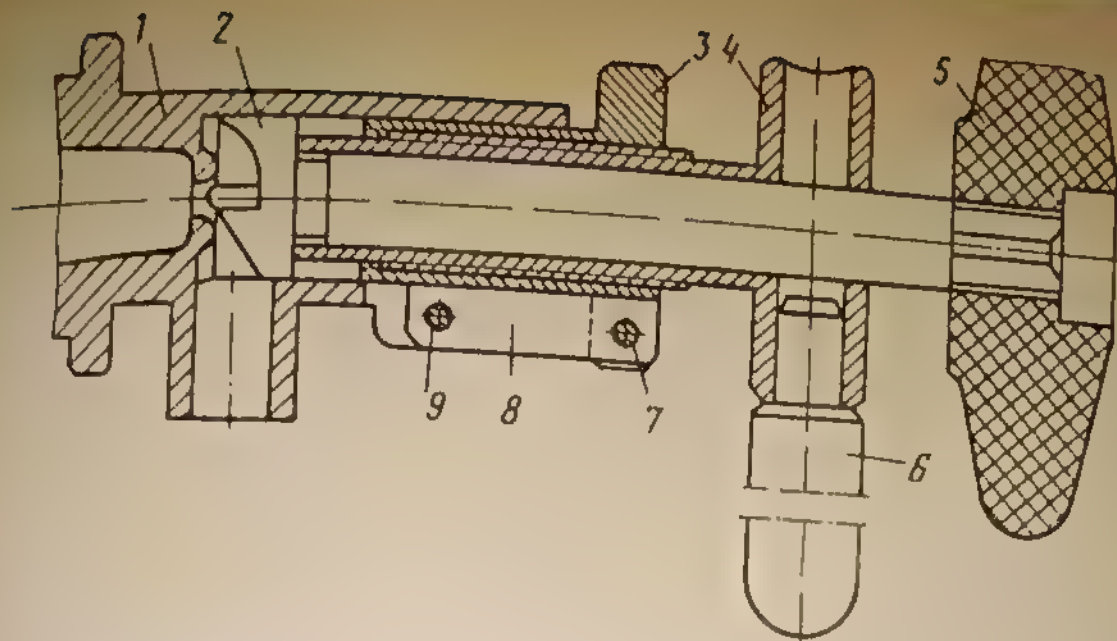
Фрезерование ножеобразного седла в корпусе поплавкового клапана противодавления
